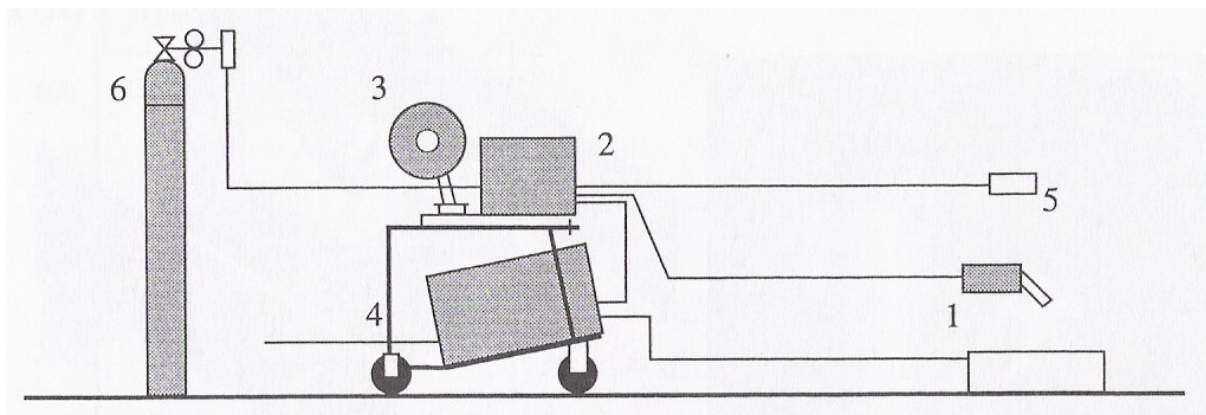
Schéma svařování v ochranné atmosféře tavící se elektrodou [2]
